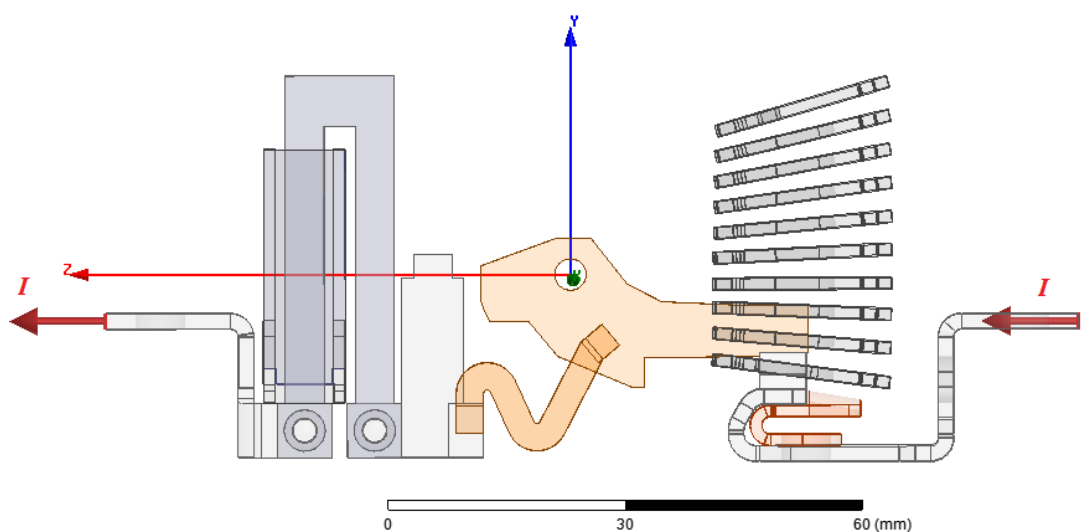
9 Vysítovaný 3D model proudovodné dráhy jističe BC 160
